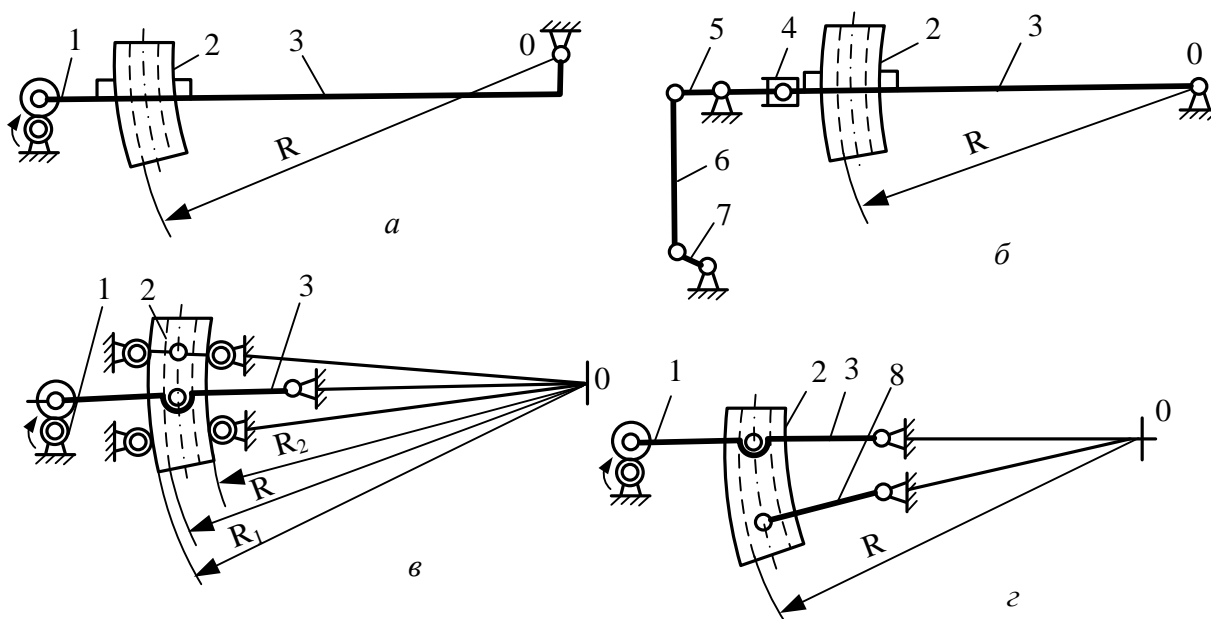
Кинематическая схема механизмов качания кристаллизатора: а – рычажно-кулачковый механизм; б – рычажно-кулисовый механизм; в – рычажно-кулачковый механизм с перемещением кристаллизатора в роликовых направляющих; г – рычажно-кулачковый механизм с приближенным воспроизводством круговой траектории движения кристаллизатора; 1 – кулачковый механизм; 2 – кристаллизатор; 3 – несущая рама; 4 – кулиса; 5 – двуплечный рычаг; 6 – шатун; 7 – эксцентрик; 8 – коромысло
